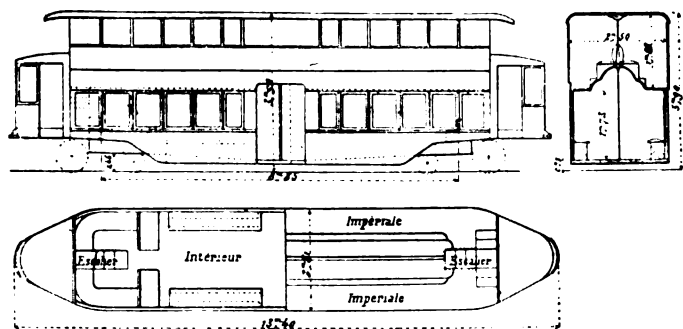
Vista, sezione e pianta delle nuove vetture delle tramvie di New-York.
